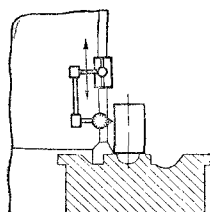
Проверка перпендикулярности направляющих фрезерной головки к консоли фрезерного станка.
